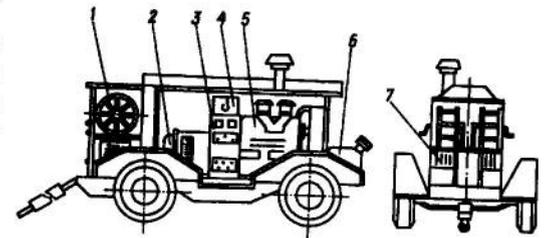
Зварювальний агрегат АСДП-500Г:
